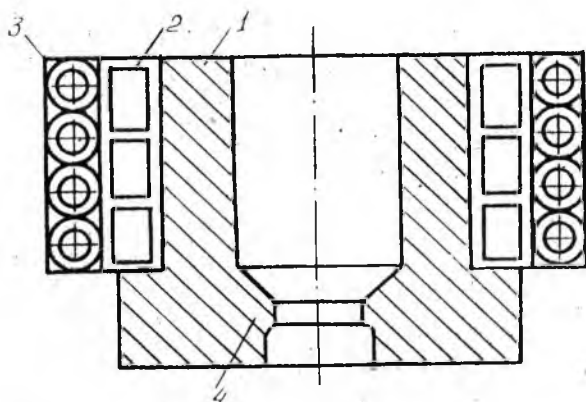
Штампы для выдавливания: 1 — контейнер, 2 — матрица, 3 — нагревательный элемент, 4 — охлаждающий элемент
